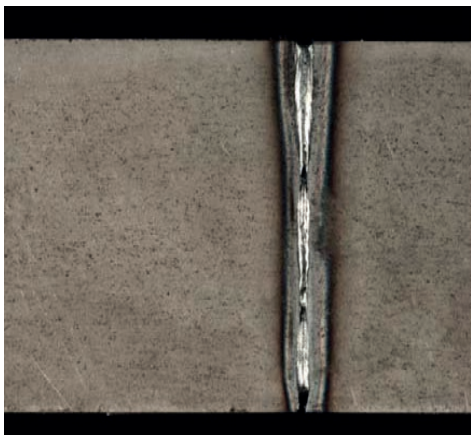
Розірваний зварний шов заготовки А – форми (406)
